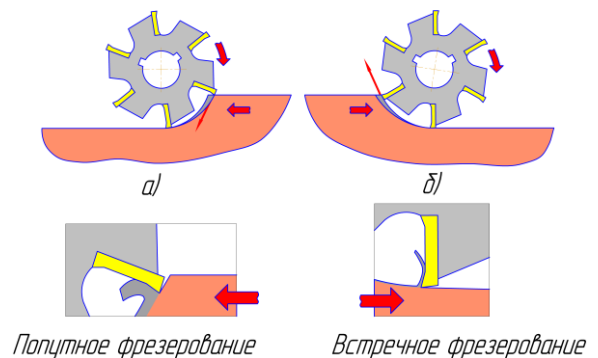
Способы фрезерования, определяемые направлением движения заготовки относительно инструмента
